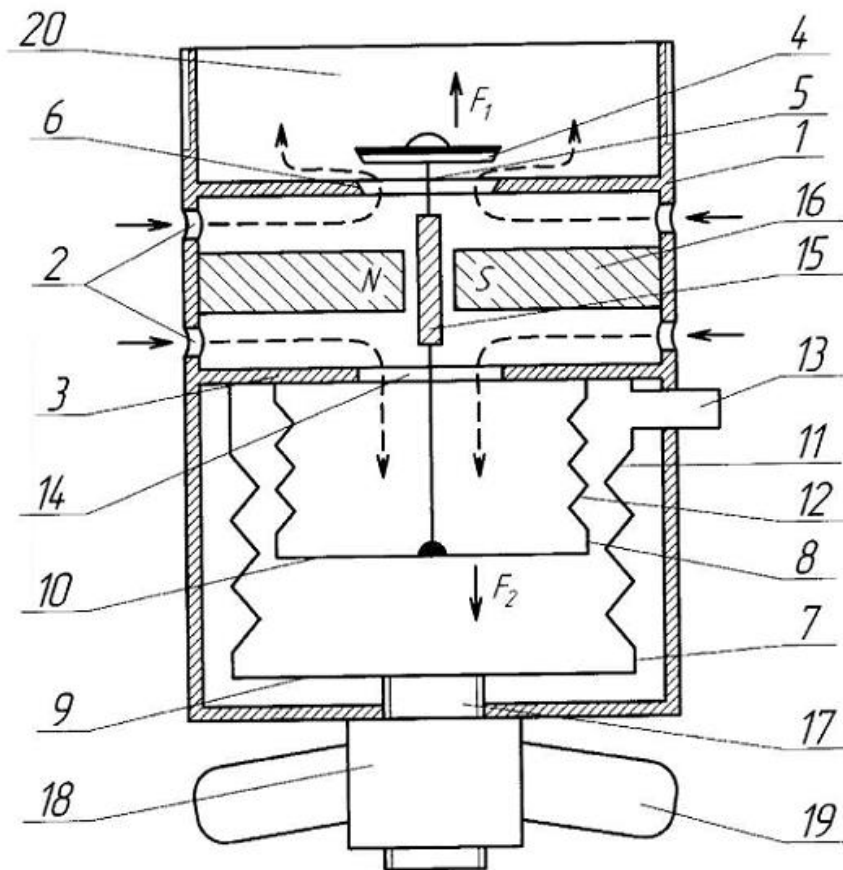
Регулятор вакууму доїльного агрегату: 1 – корпус; 2 – отвори бокові; 3 – переділка; 4 – клапан; 5 – шток; 6 – сідло клапана; 7 – сільфон зовнішній; 8 – сільфон внутрішній; 9, 10 – робочі пласкі поверхні; 11, 12 – гофровані бокові поверхні; 13 – патрубок; 14 – отвір сполучний; 15 – короткозамкнений виток пластини; 16 – магніт постійний; 17 – гвинт; 18 – гайка; 19 – пелюстка; 20 – патрубок вакуум-проводу
